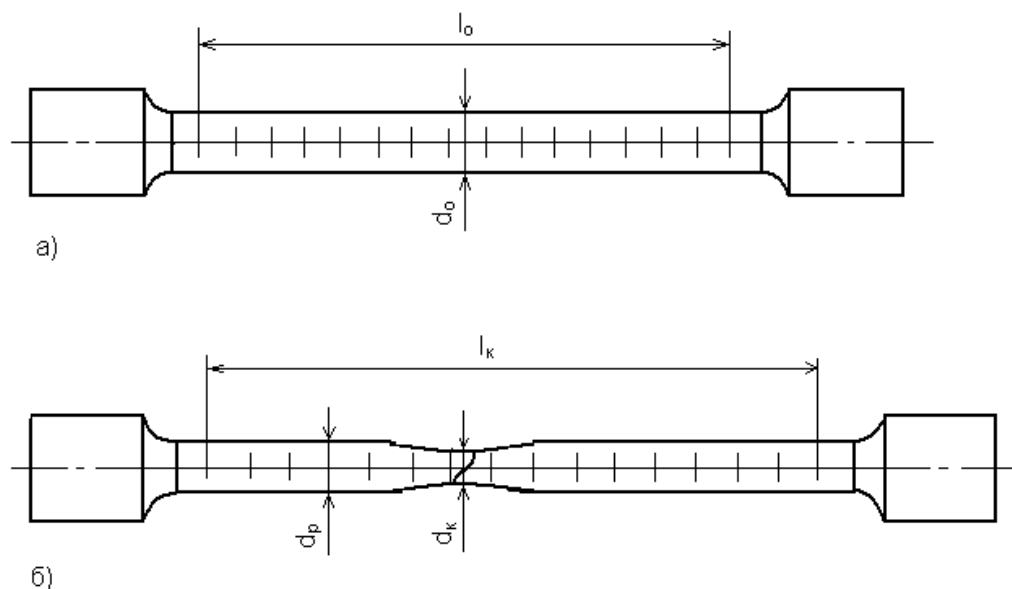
Цилиндрический образец для испытаний на растяжение: а) – до испытаний, б) – после разрушения
